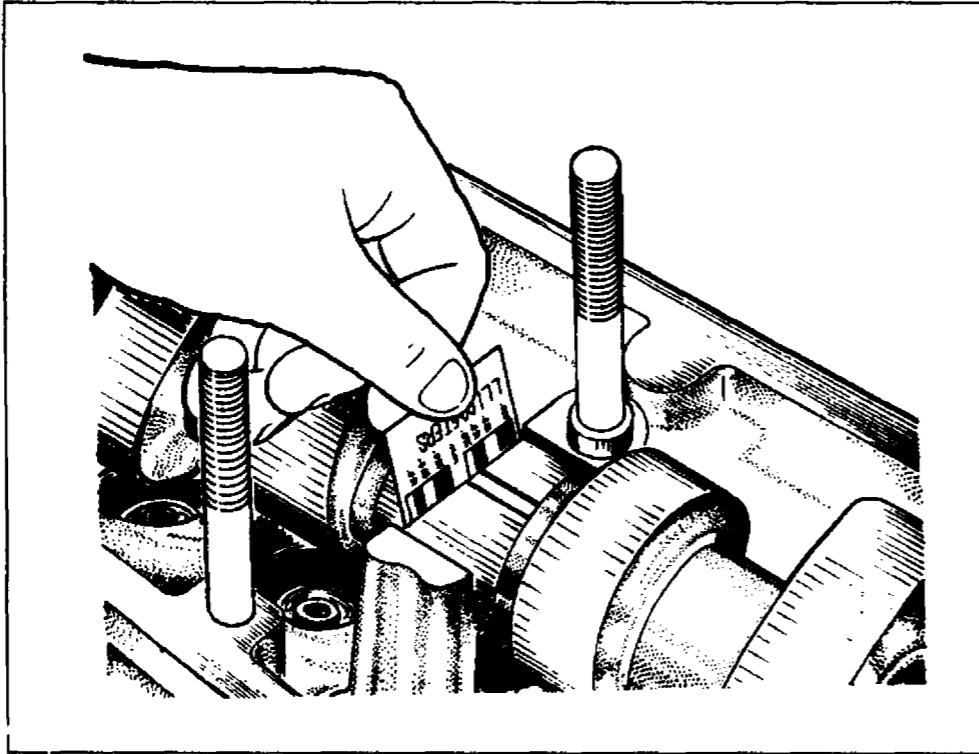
Измерение зазора между шейками распределительного вала и корпусами подшипников
